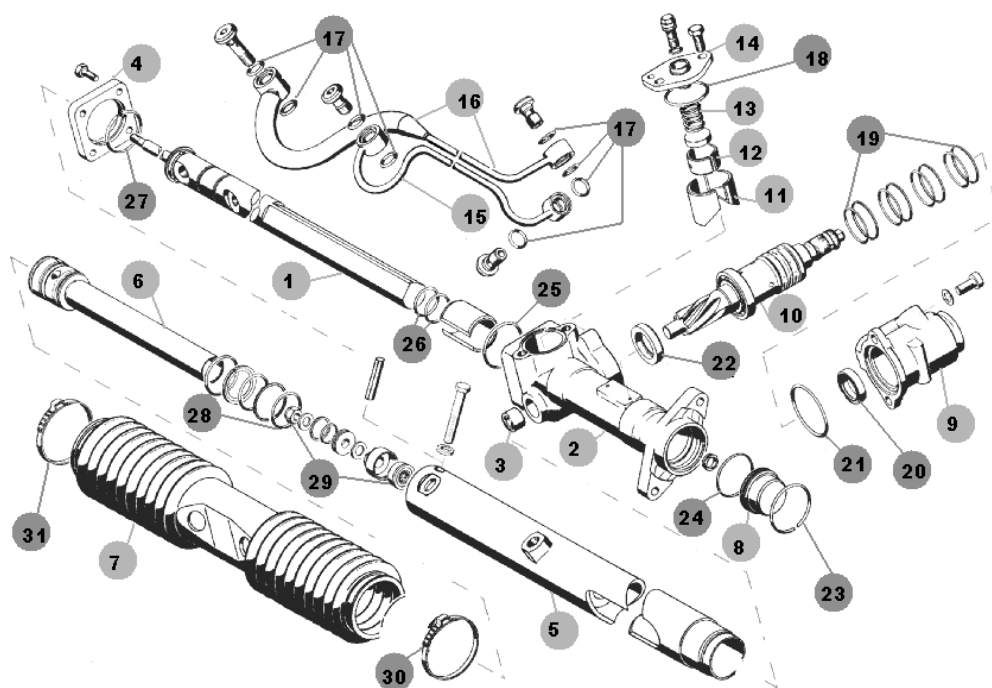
Пристрій рульової рейки без серватроніка 2-й вигляд
